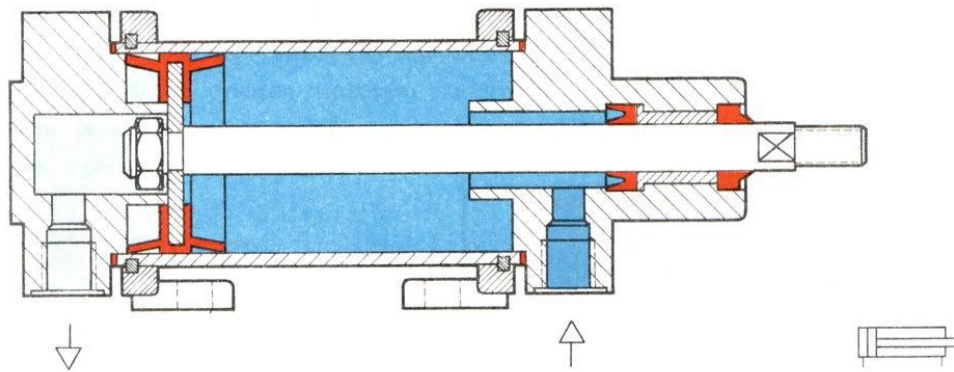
Řez jednočinným pneumatickým válcem [5]
